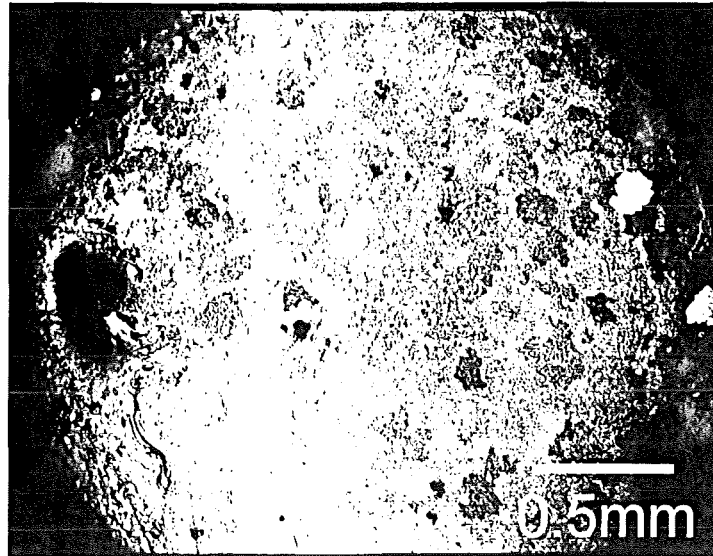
Großer Lunker (links) in der Fügezone einer widerstandsgeschweißten Probe
